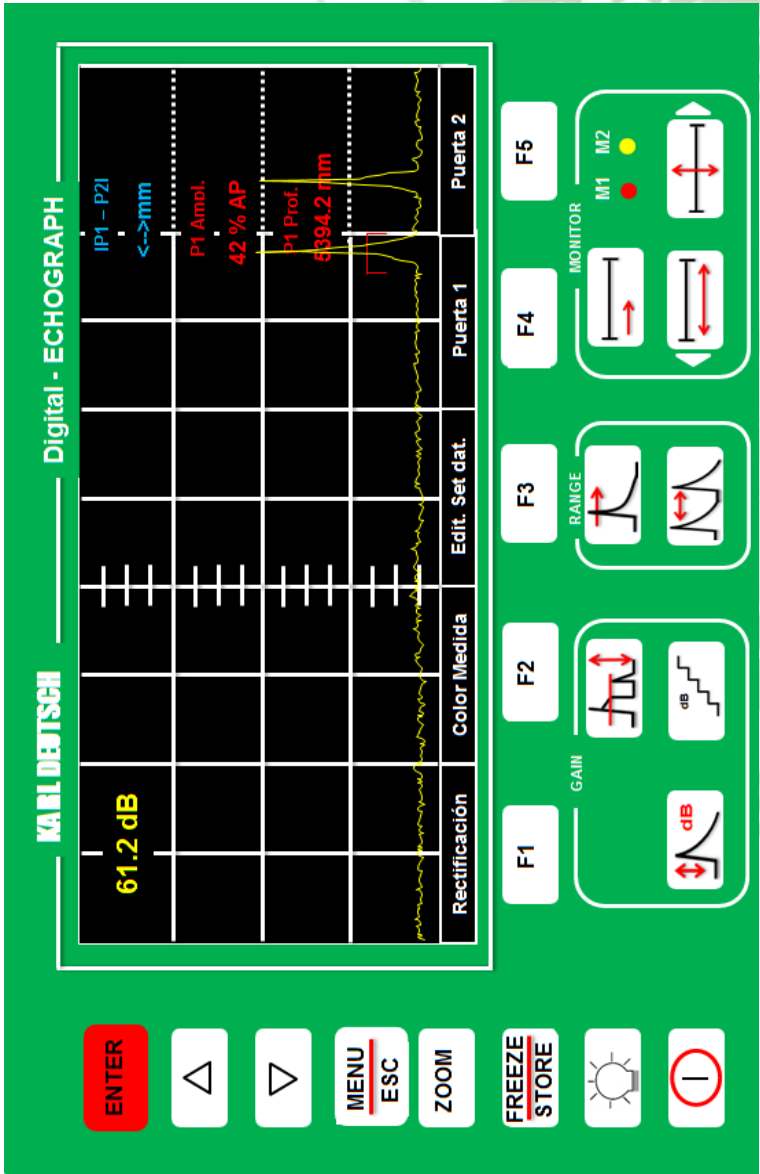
Pantalla de Inspección 2 lado derecho Fuente SPCC
